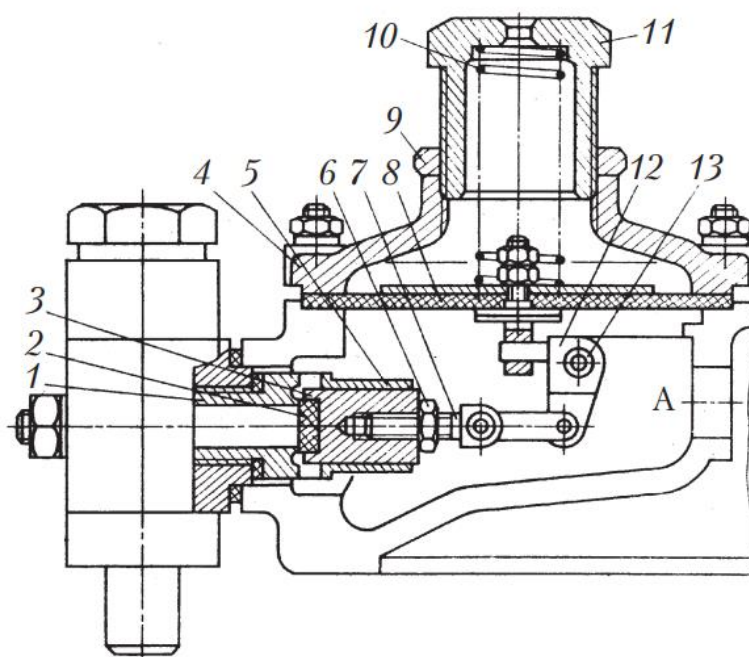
Схема первой ступени РВД: 1 — седло клапана; 2 — уплотнитель; 3 — клапан первой ступени; 4 — крышка; 5 — направляющая клапана; 6, 9 — контргайки; 7 — винт; 8 — мембрана; 10 — пружина; 11 — регулировочная гайка; 12 — рычаг; 13 — ось; А — полость камеры первой ступени
